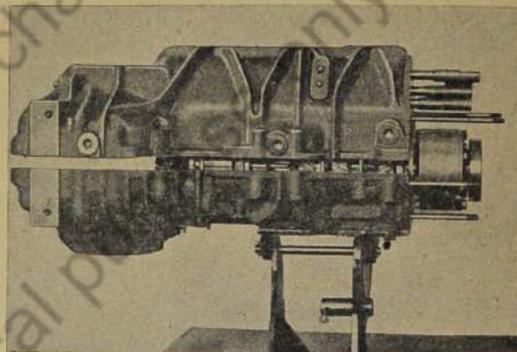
Linke Gehäusehälfte auf die rechte aufsetzen und verschrauben
